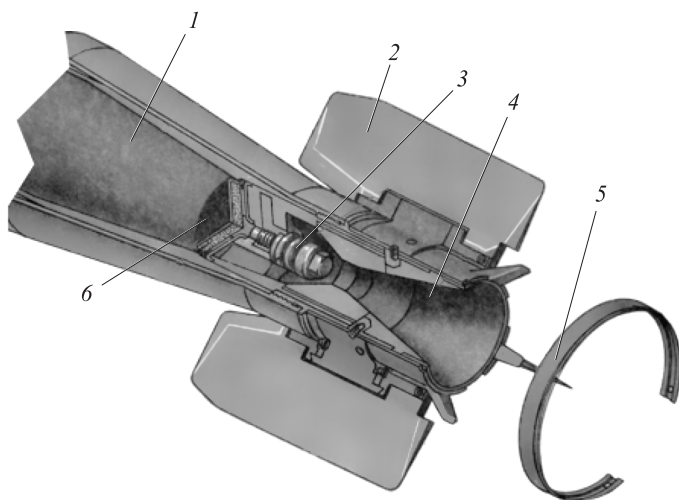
Детали блока маршевого двигателя ПЗРК 9К38 «Игла», изготовленные тиксоштамповкой [12]:
